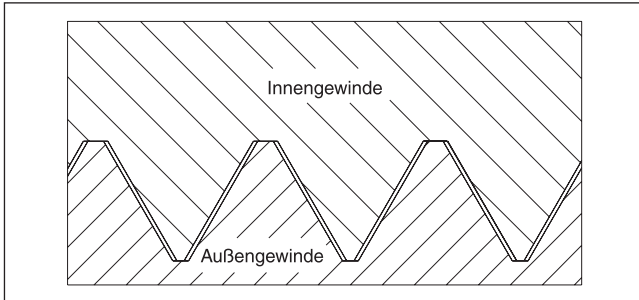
NPTF – handfest angezogener Gewindekontakt
